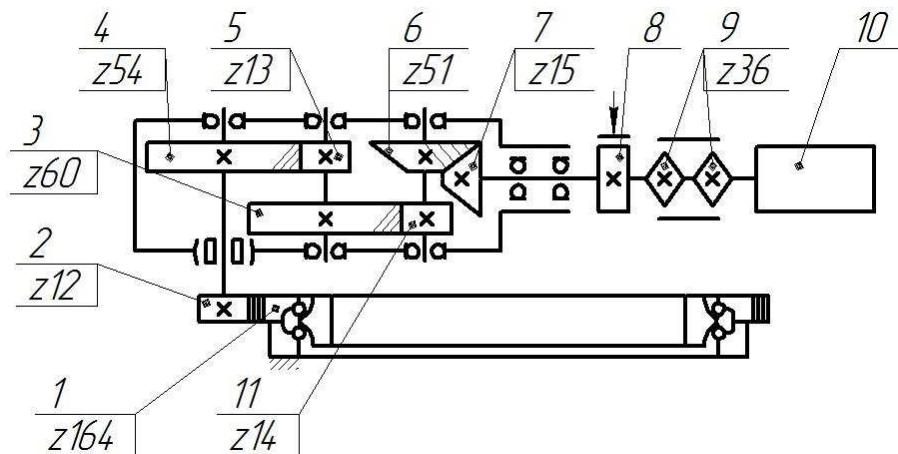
Кинематическая схема механизма поворота: 1 – зубчатый венец, 2-7, 11 – шестерни, 8 – тормоз, 9 – цепная муфта, 10 – электродвигатель
